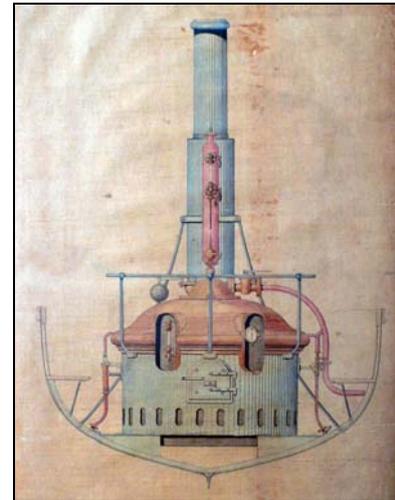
Plan restauré : coupe du canot à vapeur présentant la chaudière
